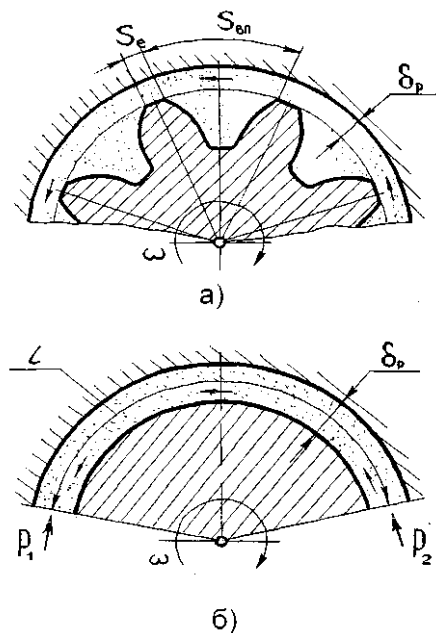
Розрахункова схеми для визначення довжини радіального зазору
